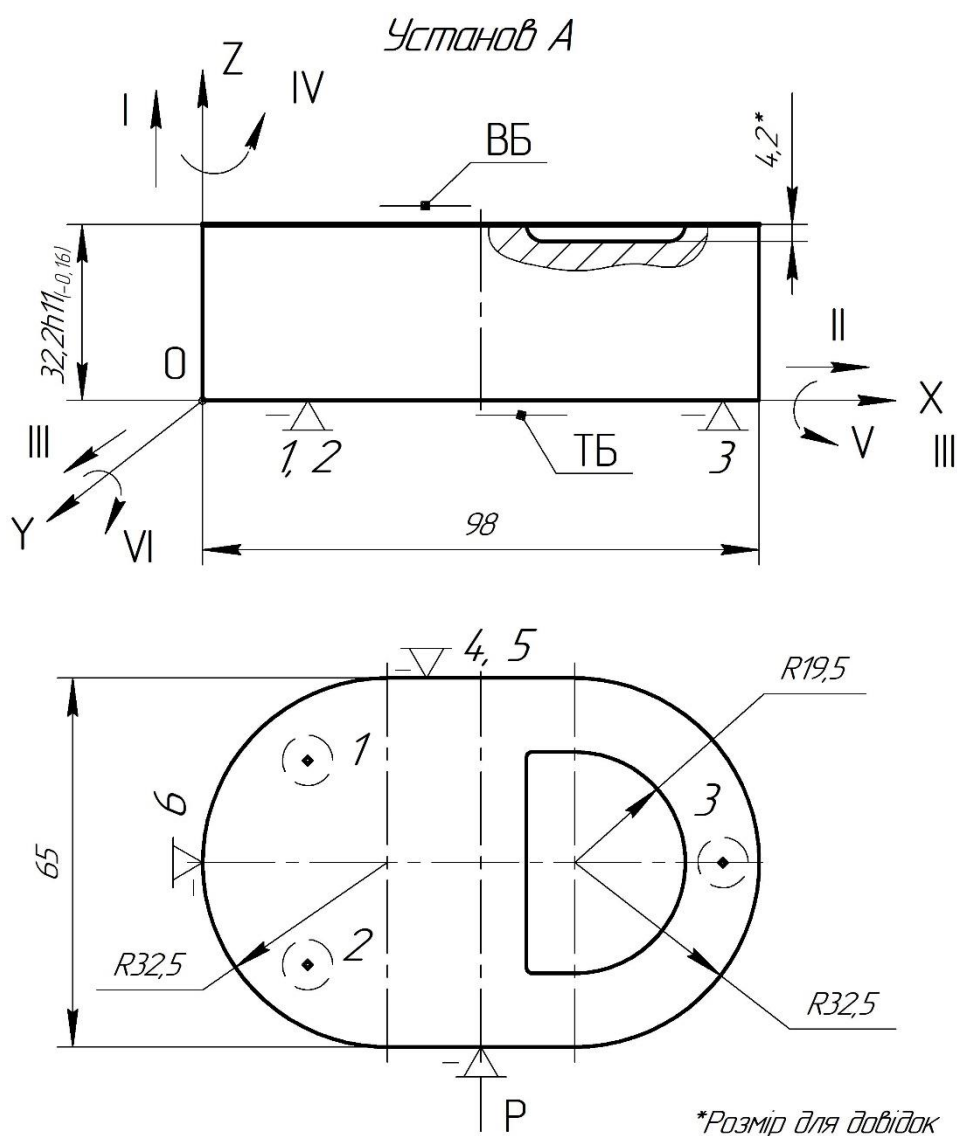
Схема установки заготовки на операції 020. Установ А
